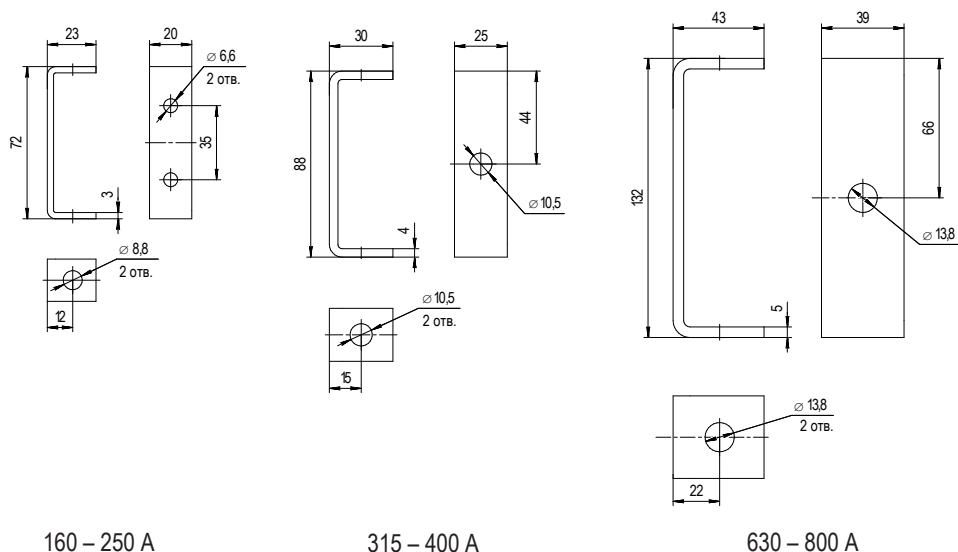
Габаритные размеры соединительных шин для реверсивных ВРК
